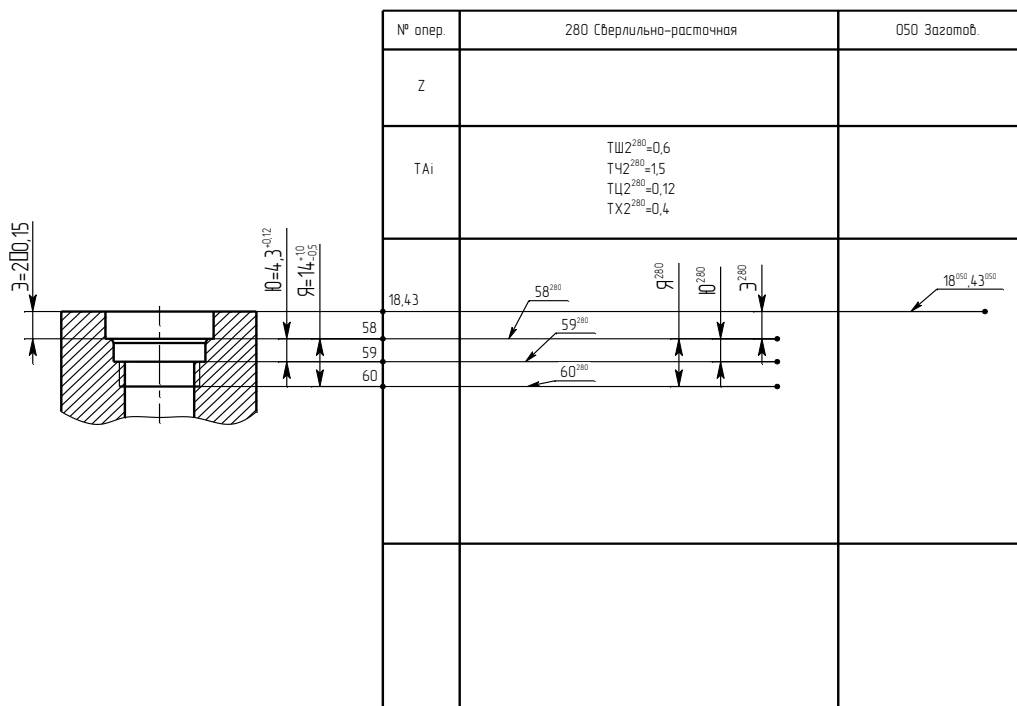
Схема линейных размеров (вид Ж)
